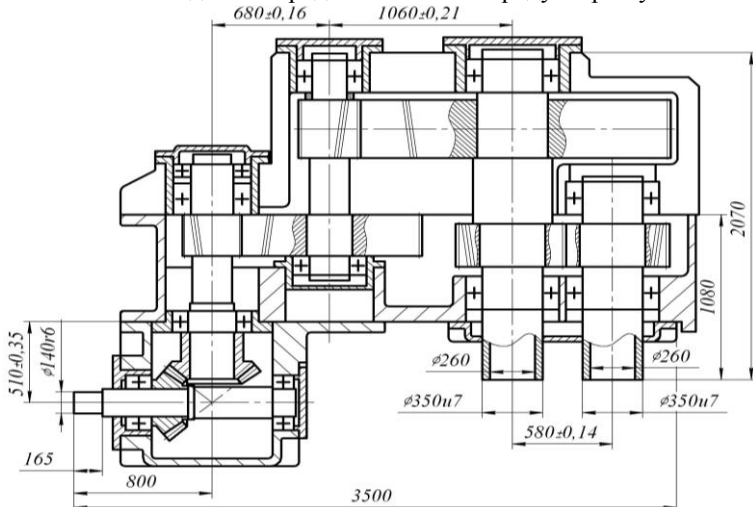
Комбинированный редуктор главного привода сортопрокатного стана
